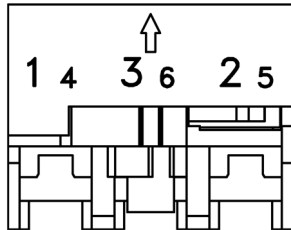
Kennzeichnung der Steckpositionen auf dem 3-fach Halter
